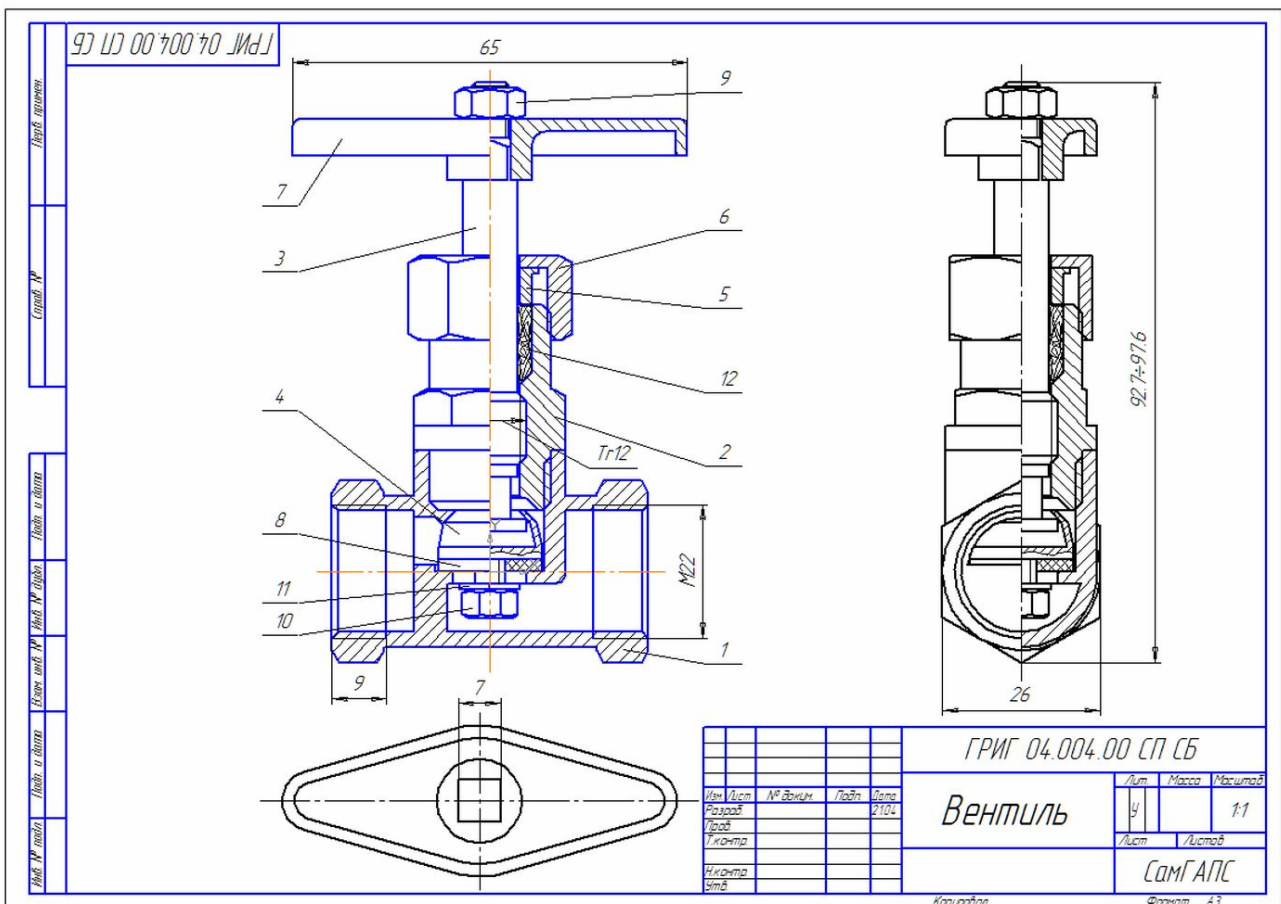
Пример сборочного чертежа изделия «Вентиль»
